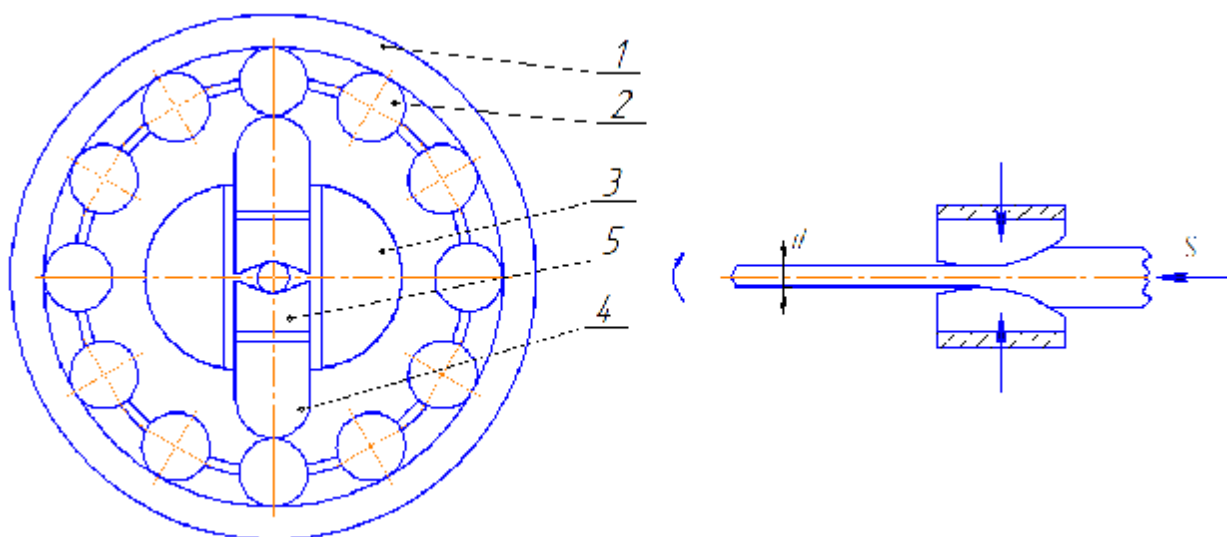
Схема механизма обжатия: 1-неподвижная обойма; 2-прижимающий ролик; 3-шпиндель; 4-ползун; 5-бойки.
